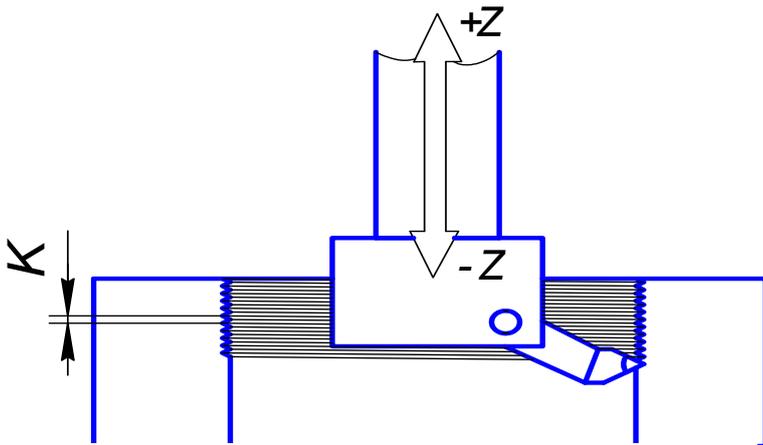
Схема нарезания резьбы резцом на фрезерном станке с ЧПУ
